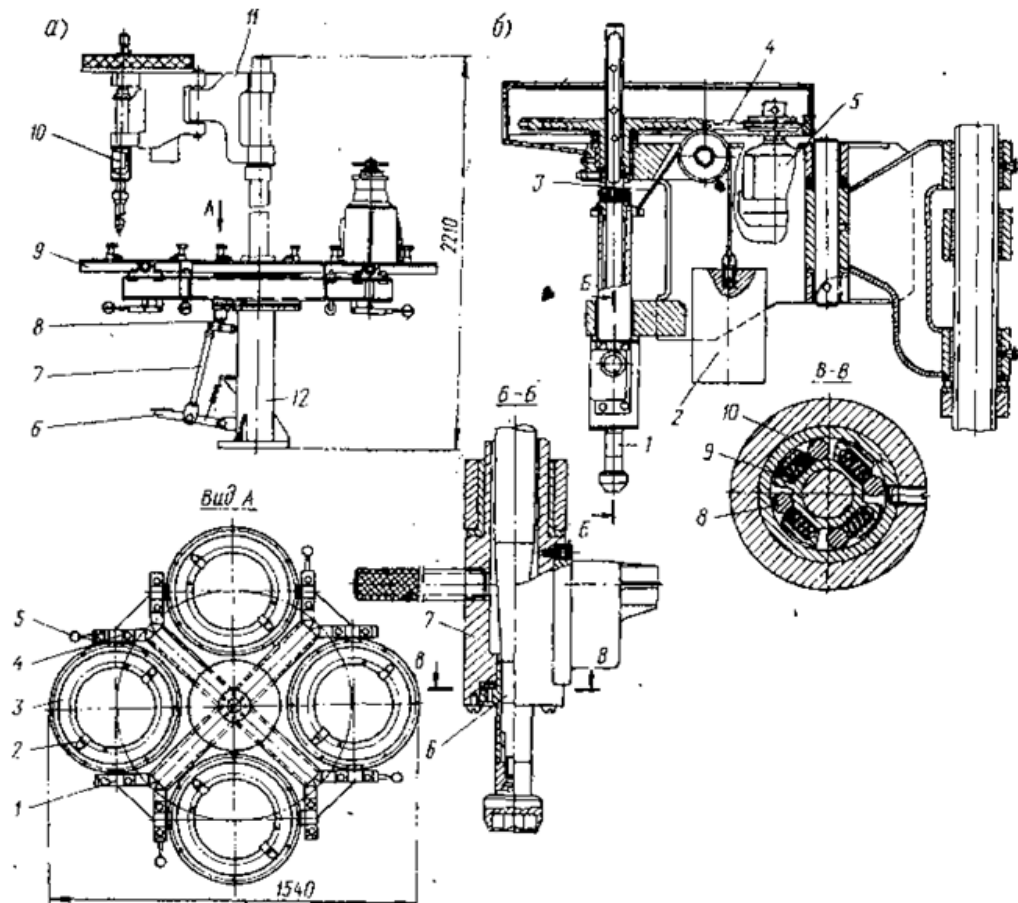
Стенд для розбори редуктора задніх мостів
